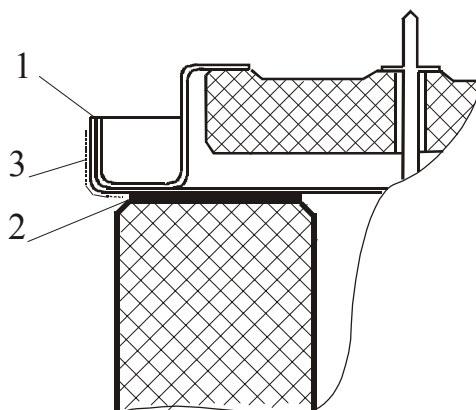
Конструкция сварочного шва 1 – сварочный шов, 2 – металло-керамический спай, 3 – растекание припоя.
